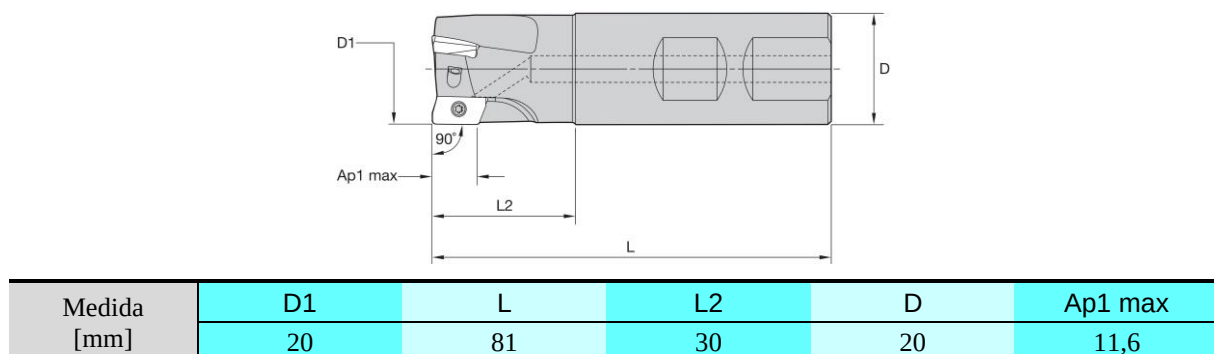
Imagem e dimensões principais do suporte utilizado no Processo de Usinagem por Fresamento.
